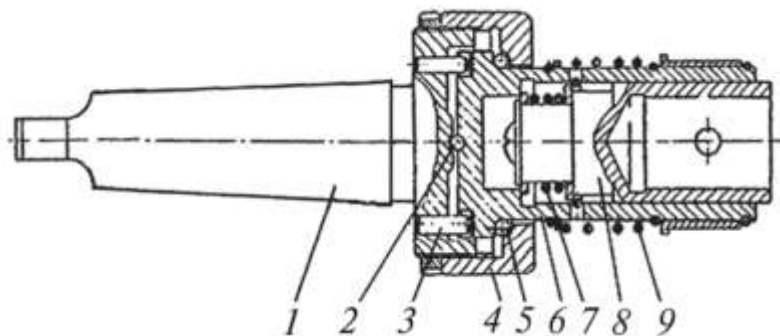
Схема різьбового патрона, що плаває і компенсує.
